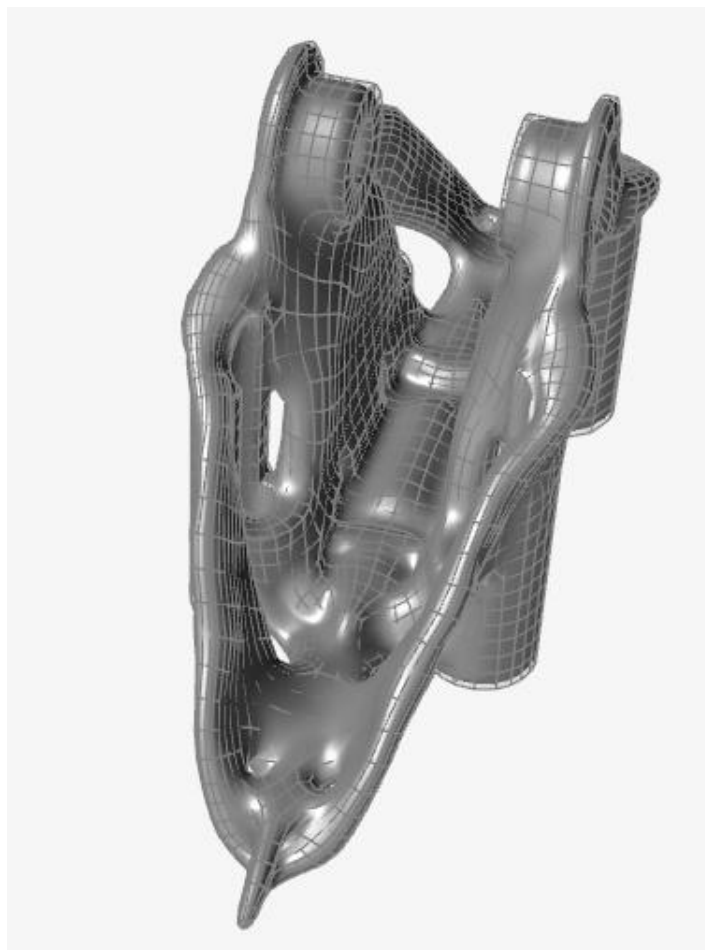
Detalle refinamiento (2). Fuente: elaboración propia
